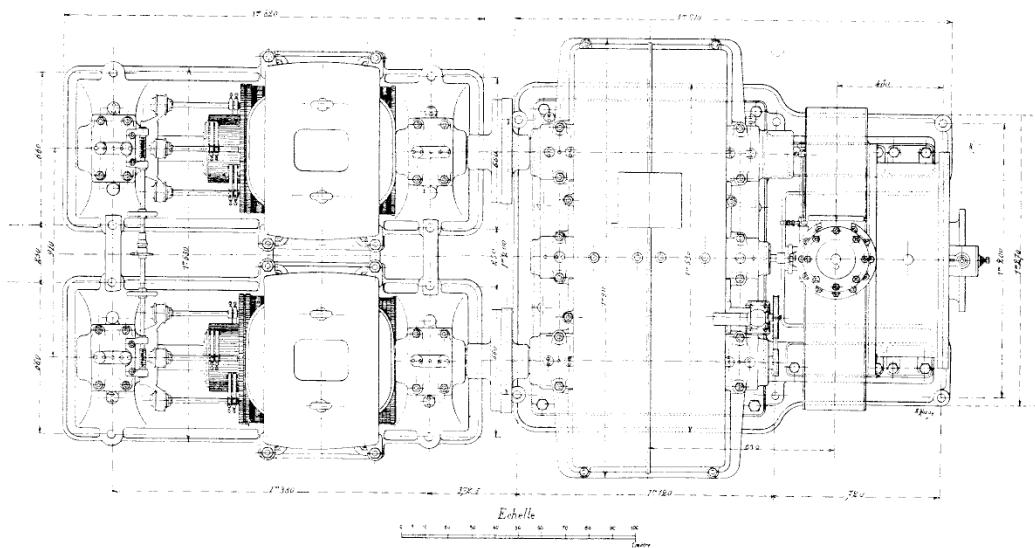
Groupe électrogène Breguet-de Laval. — Plan.
